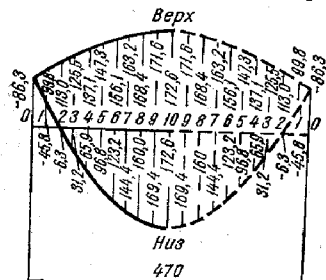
Развертка отверстия в стволе сварного тройника.
